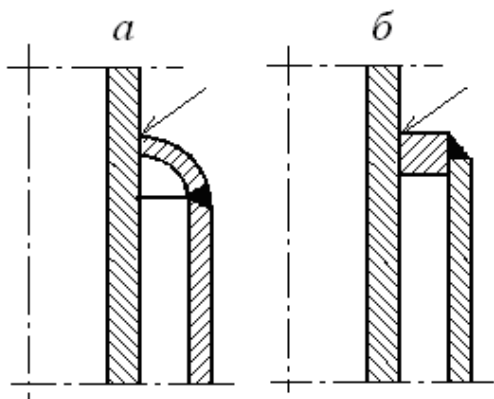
Неразъемное крепление рубашки к корпусу:
